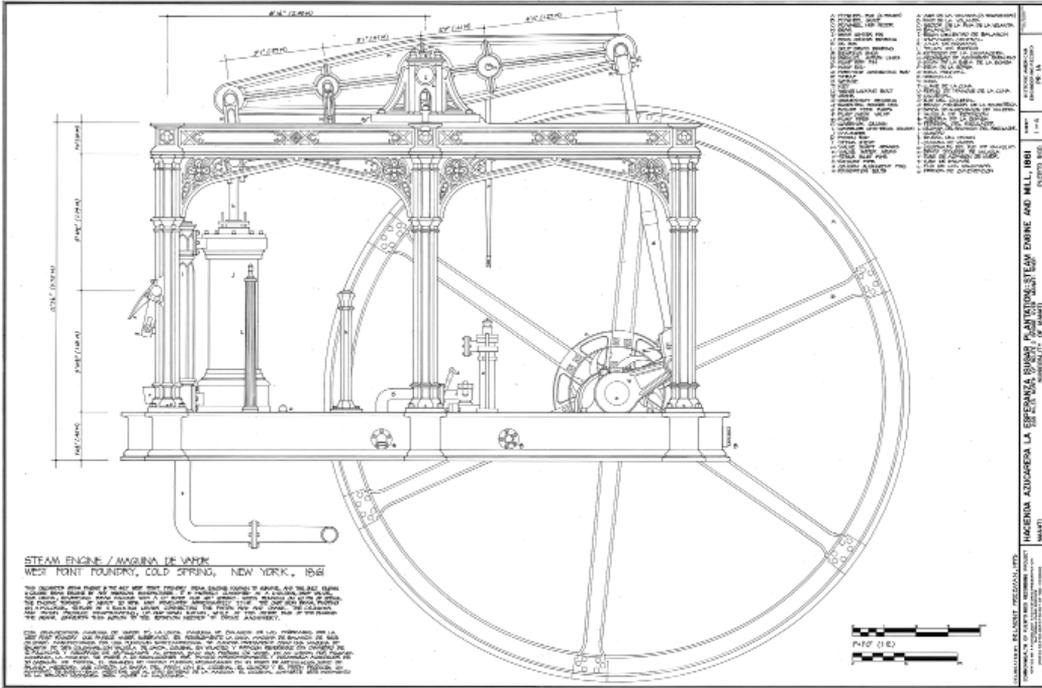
Documentación sobre la única máquina de balancín de la West Point Foundry que ha sobrevivido. (Fuente: LOC)
